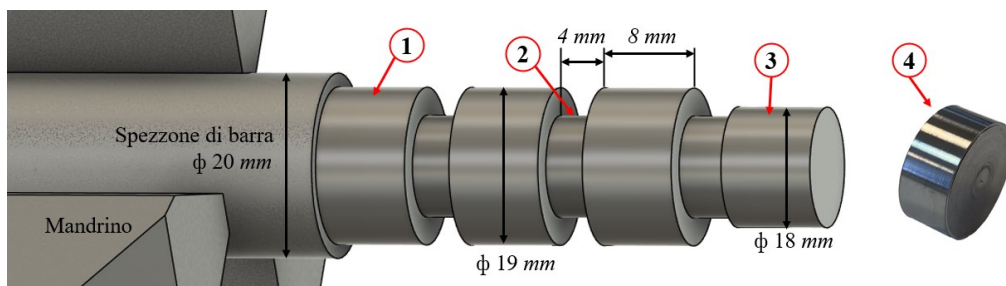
Schema delle fasi di tornitura e campione reale ottenuto dalla lavorazione con lubrificante.
